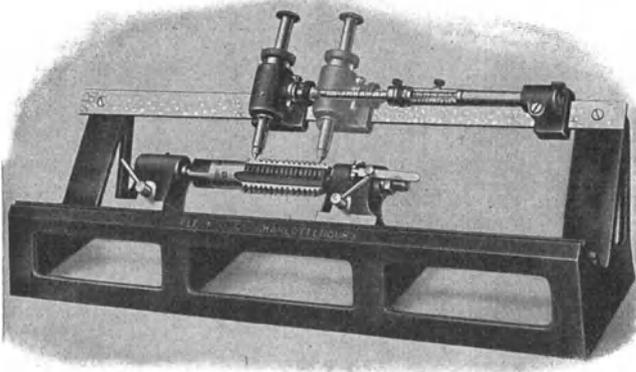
Gewindemeßapparat (Fleck & Co., Berlin).
